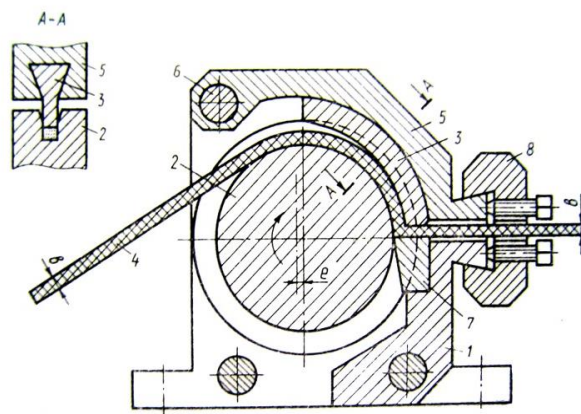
Схема и пример конструктивного исполнения инструмента для непрерывного РКУП-Конформ длинномерных заготовок [62]
